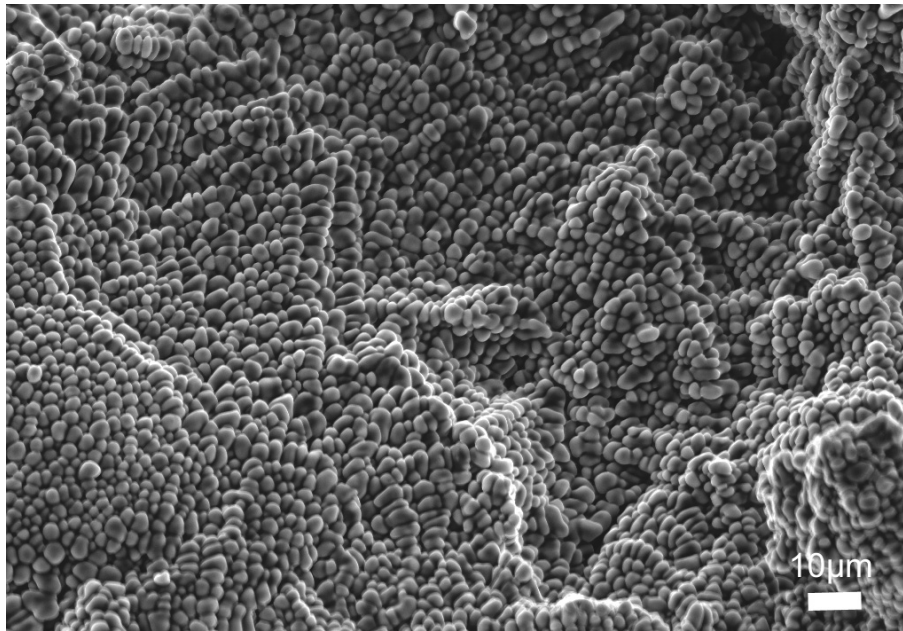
faciès de rupture en fissuration à chaud
